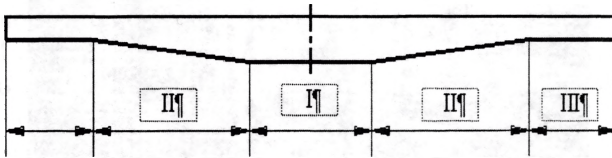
Форма профилированной заготовки малолистовой рессоры: I — центральная часть; II — параболический или клиновидный профиль; III — концевые гладкие участки
